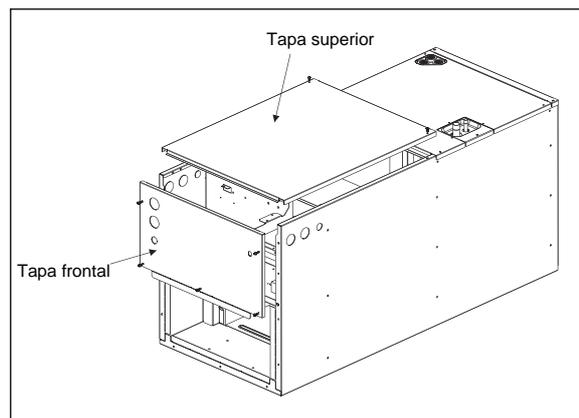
Retirar la cubierta frontal y la cubierta superior
